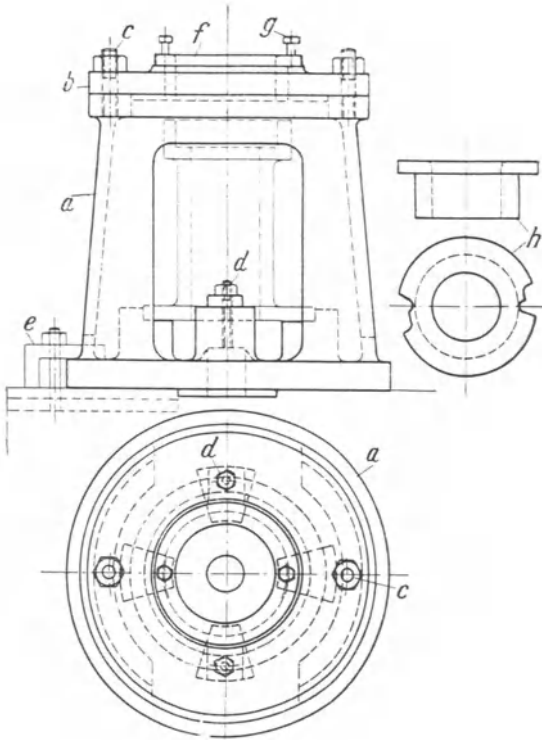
Bohrvorrichtung auf Vertikalbohrwerk für das Ausbohren von Zylinder.
